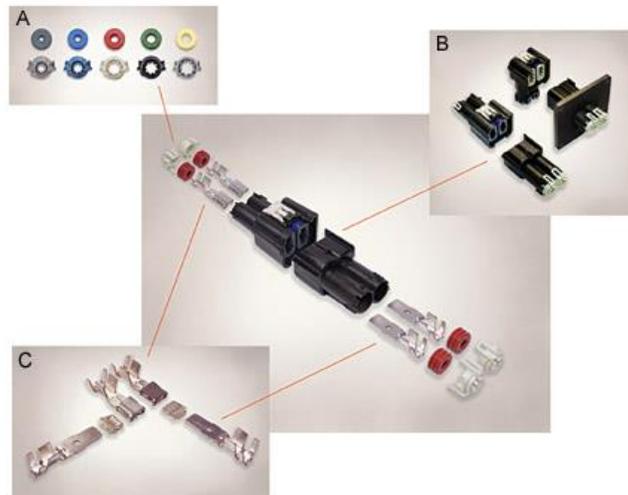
Diagrama explosivo de un conector hembra y macho.⁵
